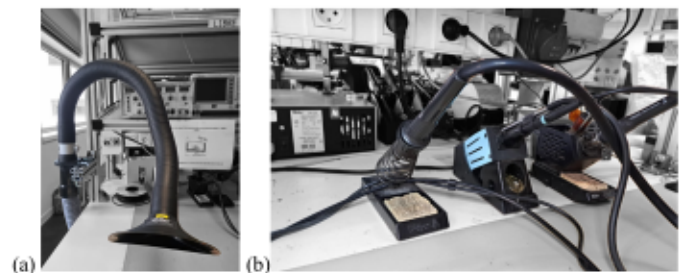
(a) extracteur de fumées, (b) station de soudure et de dessoudage.
